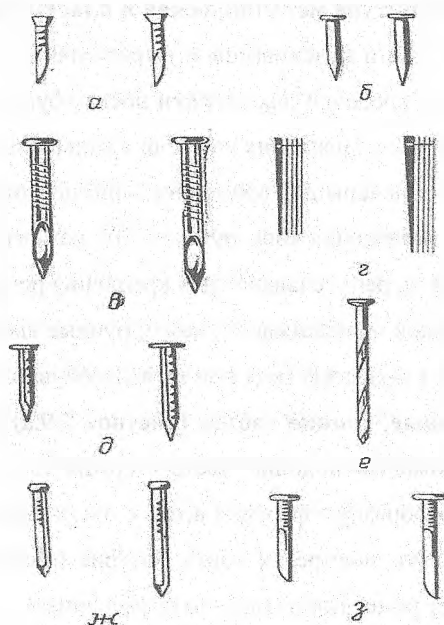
Гвозди для ремонта обуви: а – укрепительные; б – для крепления резиновых подошв; в – для крепления резиновых каблучков; г – для крепления кожаных каблучков; д – для крепления деревянных каблучков; е – для крепления пластмассовых каблучков; ж – шпильки; з – обувные тексы
